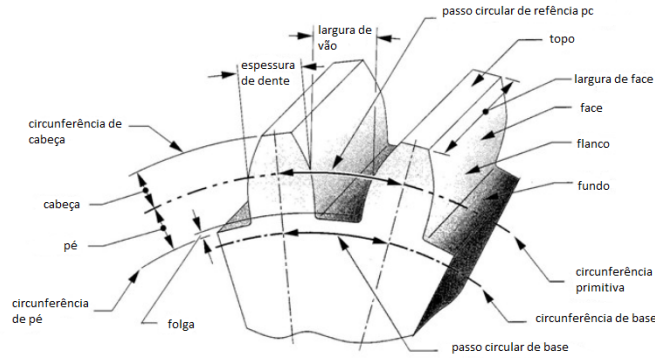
Dimensões principais de engrenagens cilíndricas. Adaptado de [37].
